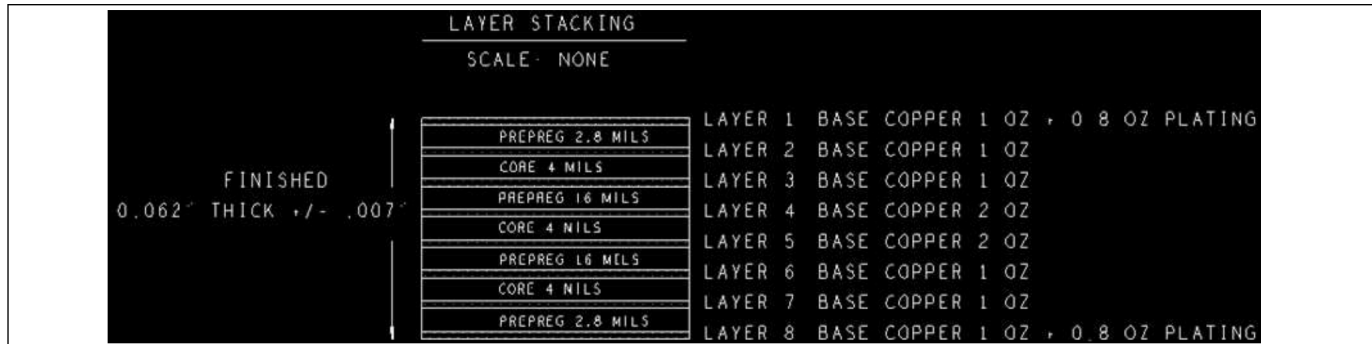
PCB 结构细节（8 层，总铜厚 11.6 盎司）
